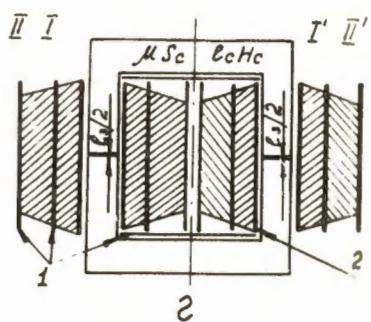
Эскиз конструкции повышающего резонансного трансформатора блока ВВП-ЗОК.
